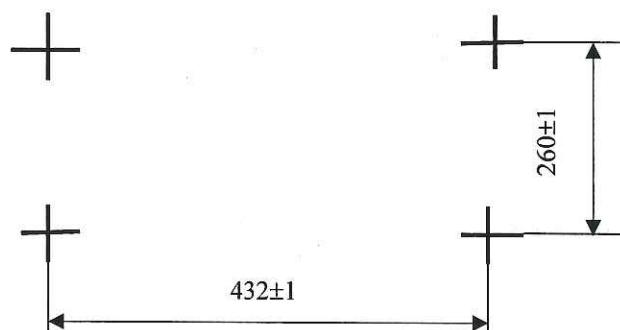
Разметка для крепления блока аккумуляторов БА-01
